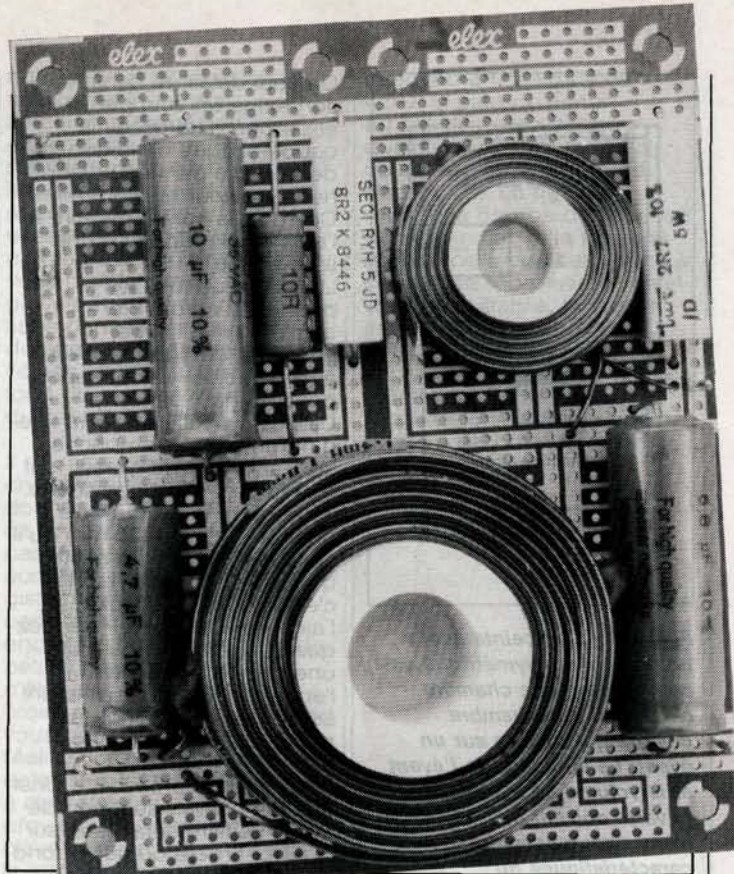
Ce filtre sera vissé sur le panneau que forme le fond du satellite. On disposera des entretoises entre la platine et le panneau du fond.
